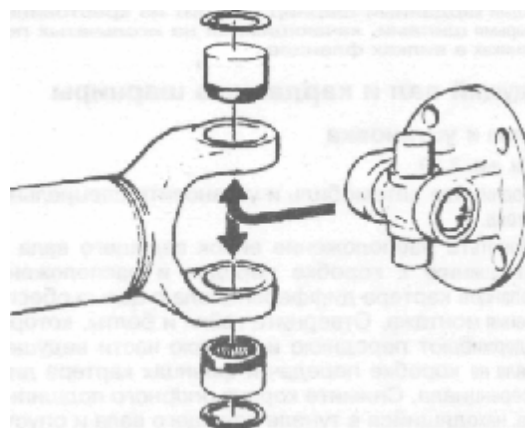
Расположение фланца и нового шарнира на ведущем валу
